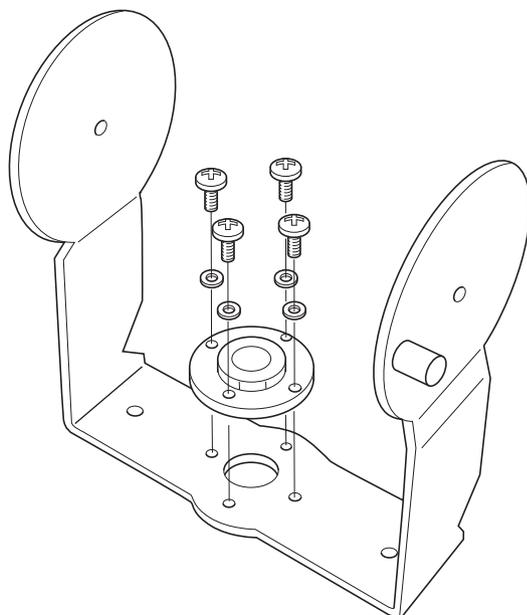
Installazione della piastra alla staffa di sospensione in caso di montaggio a muro.
